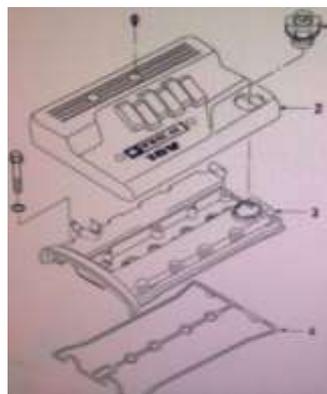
Desmontaje de Cubierta Tapa Válvulas
